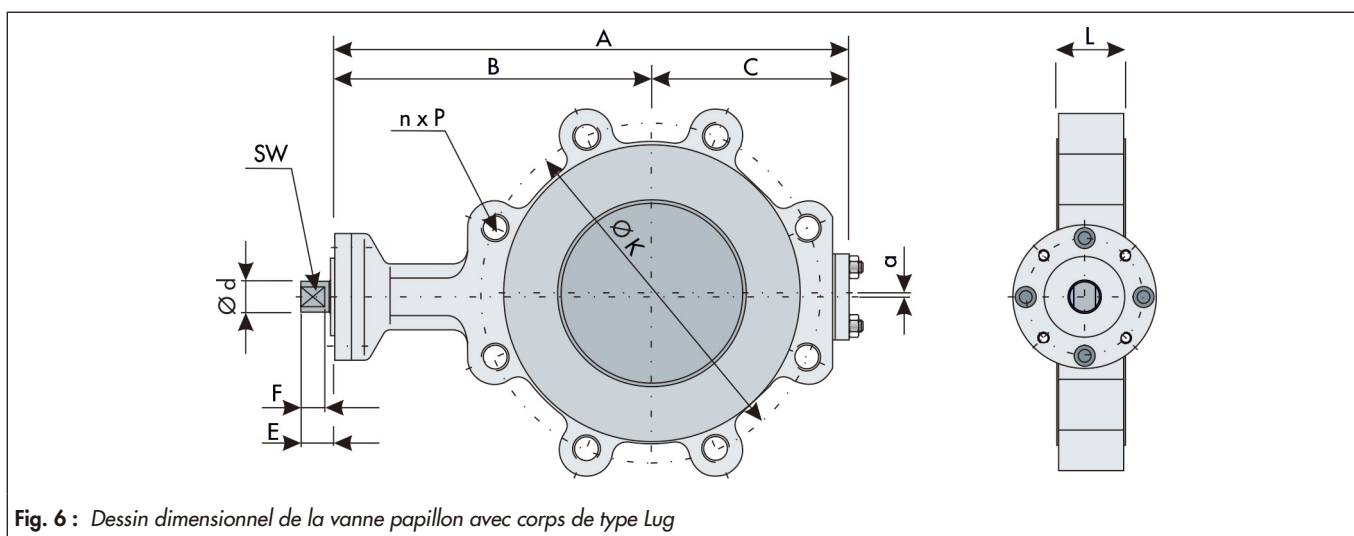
Dessin dimensionnel de la vanne papillon avec corps de type Lug
